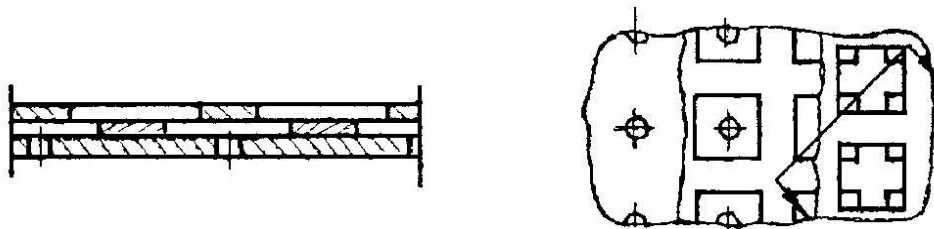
Конструкція багат шарової перфорованої решітки
